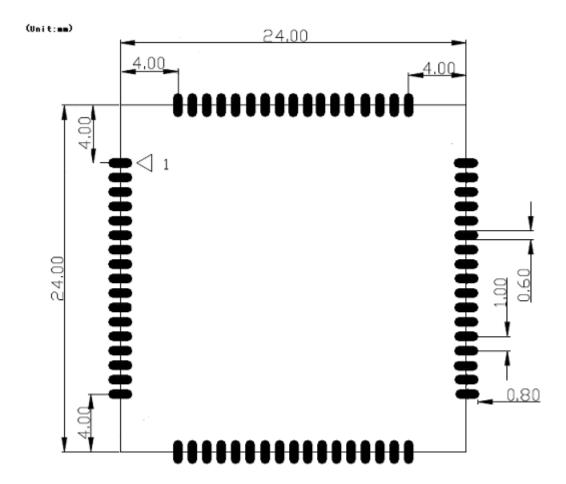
推荐GU900E 焊接封装尺寸示意图(单位: mm)
